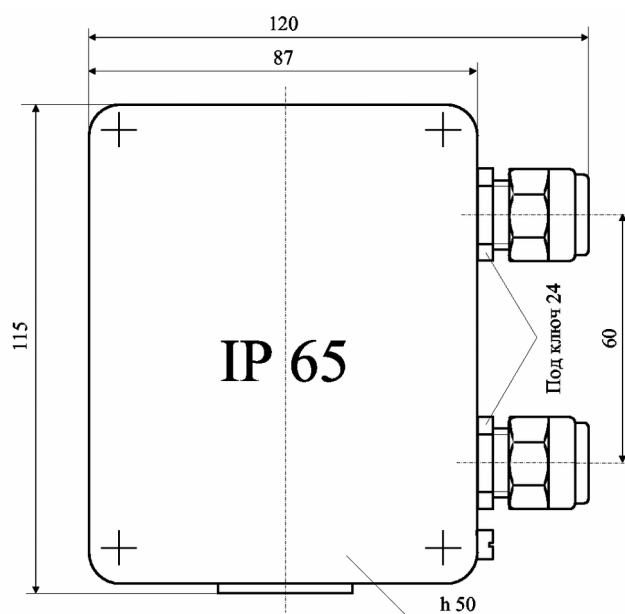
Корпус «Д» ЭБ ПП из алюминиевого сплава
